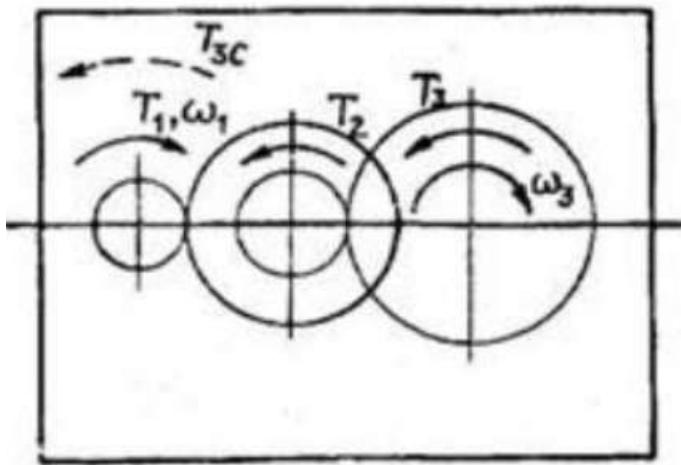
Крутящие моменты в двухступенчатом цилиндрическом редукторе
